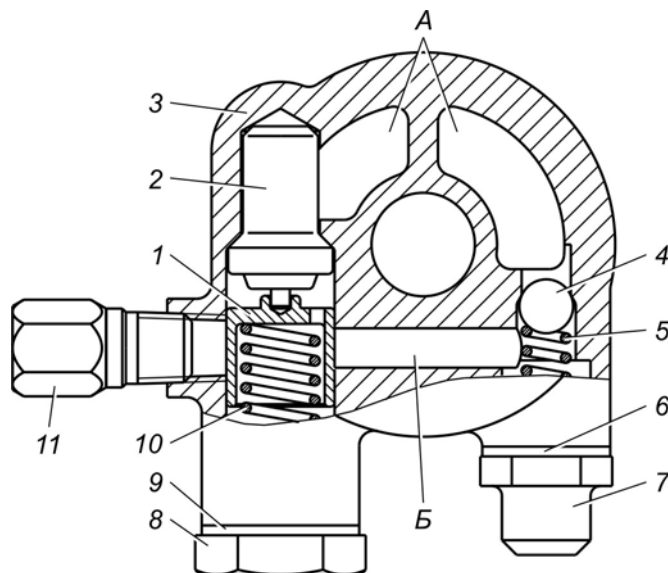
Термоклаван: 1 – плунжер; 2 – термосиловой датчик; 3 – корпус термоклавана; 4 – шарик; 5 – пружина шарикового клавана; 6 – прокладка; 7, 8 – пробка; 9 – прокладка; 10 – пружина плунжера; 11 – штуцер
